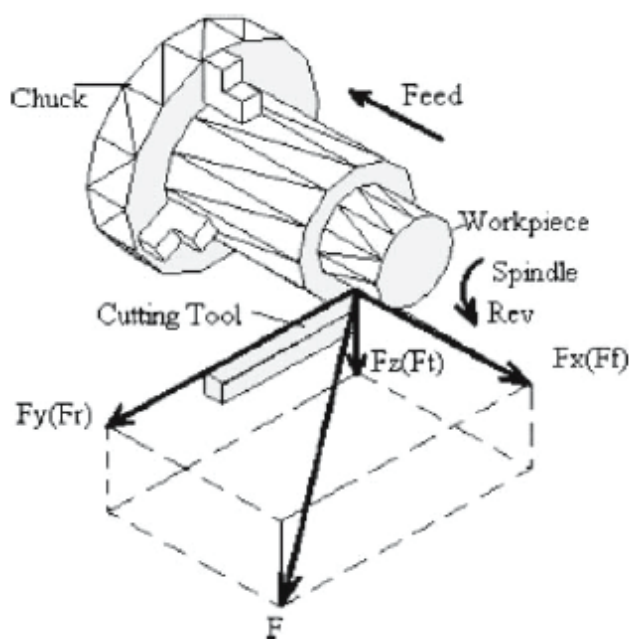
Fuerzas de corte en una operación de torneado (imagen tomada de [254])
